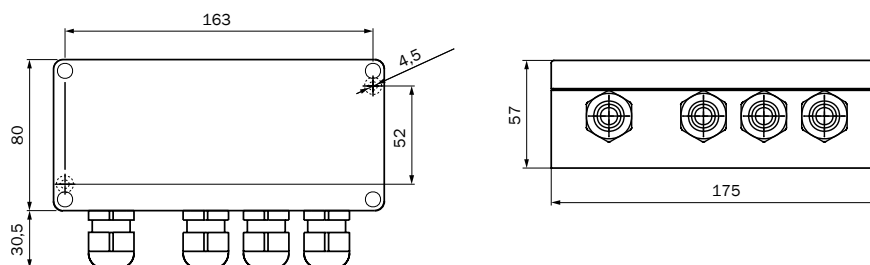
Dimensions du boîtier de raccordement (cotes en mm)
